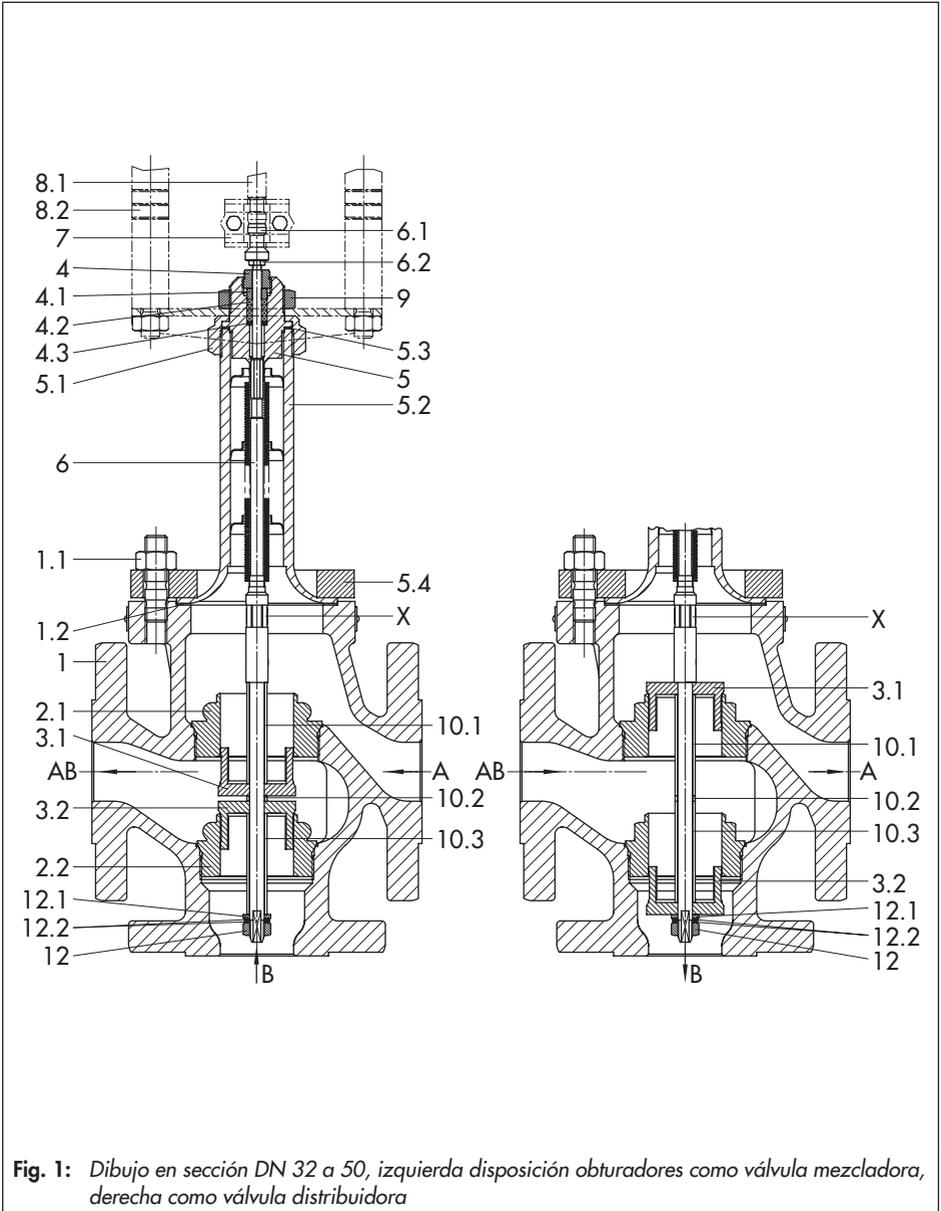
Dibujo en sección DN 32 a 50, izquierda disposición obturadores como válvula mezcladora, derecha como válvula distribuidora
